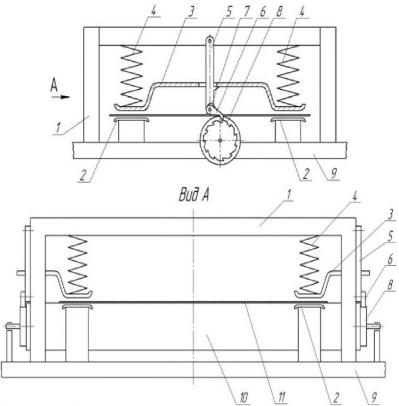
Устройство для улавливания ленты конвейера в случае ее обрыва
